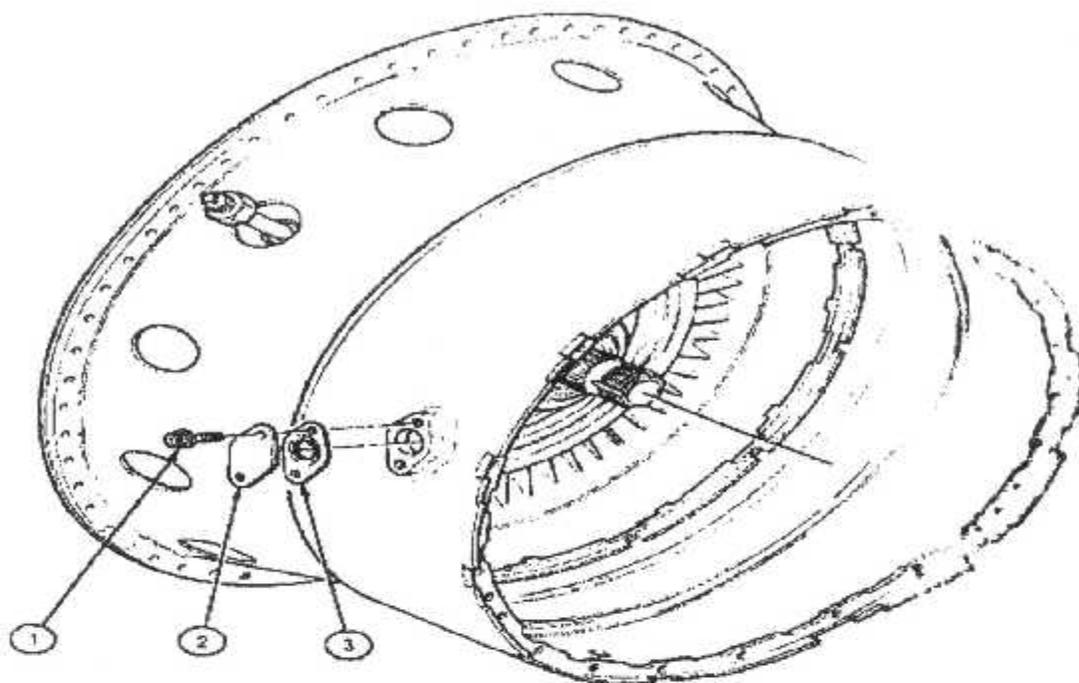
Inspection boroscopique de l'assemblage stator et les aubes du 1^{er} étage de la turbine libre.
